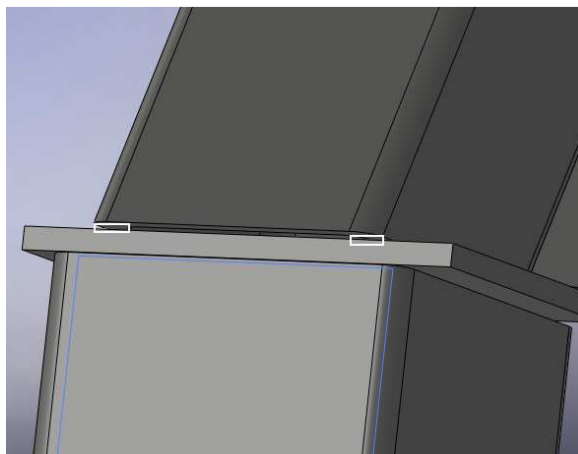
Locais onde se prevê defeitos de soldadura
